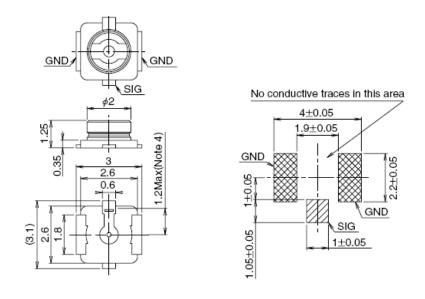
U.FL-R-SMT 连接器尺寸(单位:毫米)
